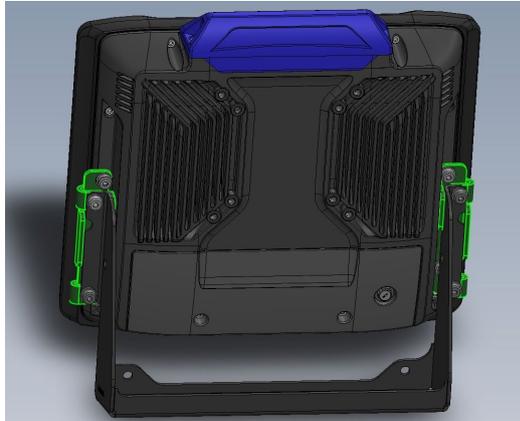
Montagebügel mit Adapter am DLT-V73A
